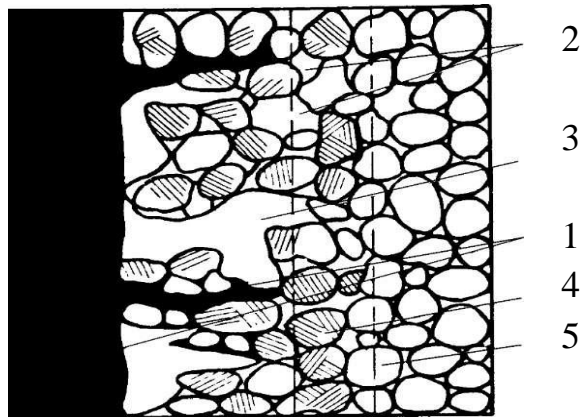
Строение контактной зоны: 1 - отливка и сплав, проникший в поры или трещины формы; 2 - поры; 3 - новообразования; 4 - видоизмененные зерна песка; 5 - малоизмененные зерна песка
